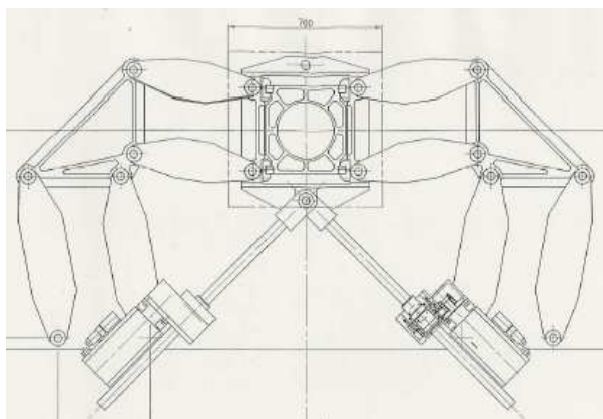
Redundantní varianta PH1 inspirovaná mechanismem Dyna-M
